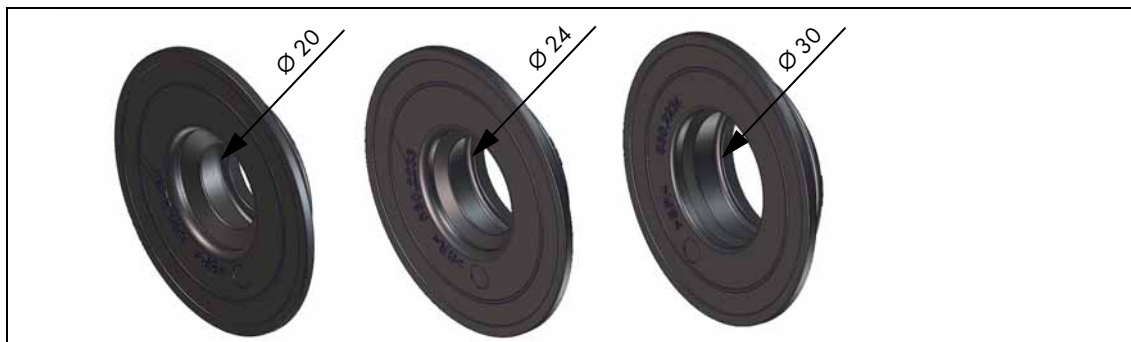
Dichtgummi für Gasdüsenaußendurchmesser
